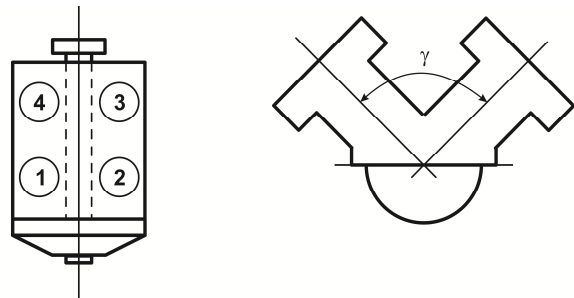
Общая схема базового двигателя 4Ч 7,6×6,6
